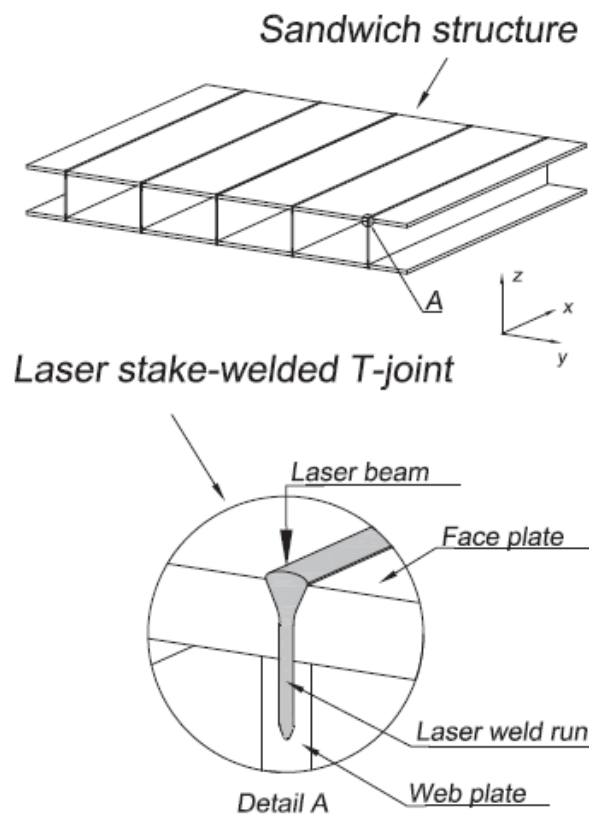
esempio di *stake welding web-core steel sandwich panels
